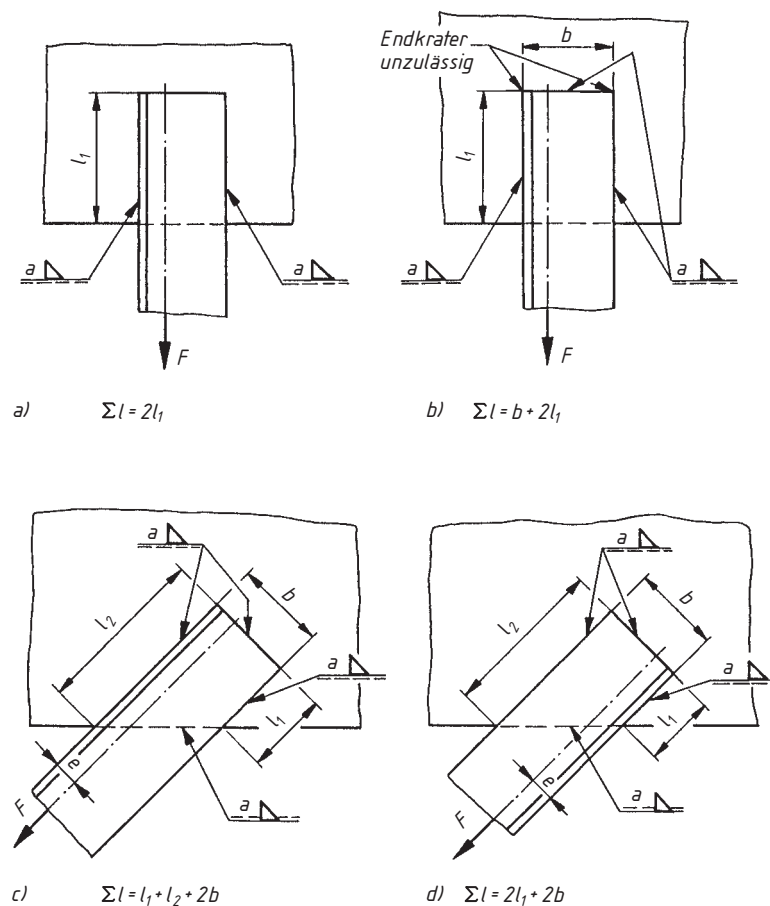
Rechnerische Schweißnahtlänge bei unmittelbaren Stabanschlüssen im Stahlbau (DIN 18 800-1) a) mit Flankenkehlnähten, b) mit Stirn- und Flankenkehlnähten, c) mit ringsumlaufender Kehlnaht: Schwerachse näher zur längeren Naht ($e < b/2$), d) mit ringsumlaufender Kehlnaht: Schwerachse näher zur kürzeren Naht ($e < b/2$).
